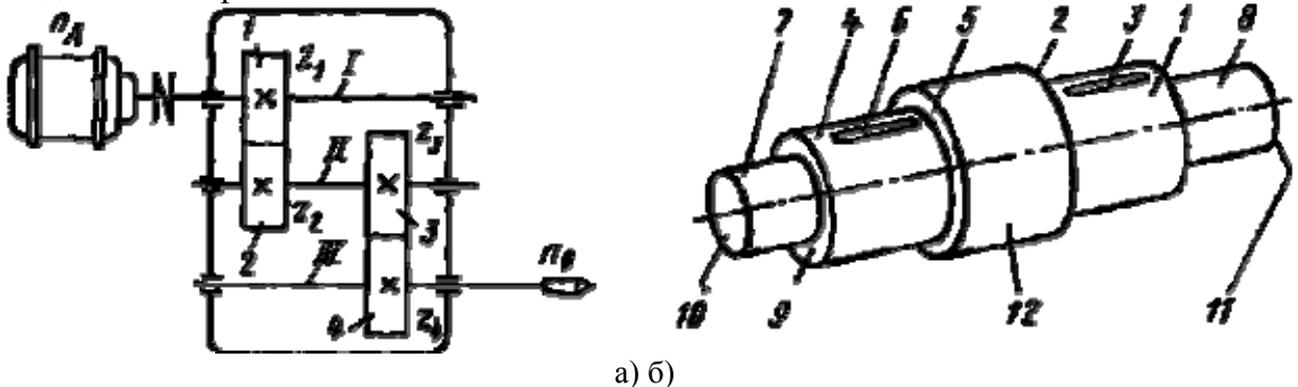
Кинематическая схема редуктора (а) и конструктивные формы вала II (б)
